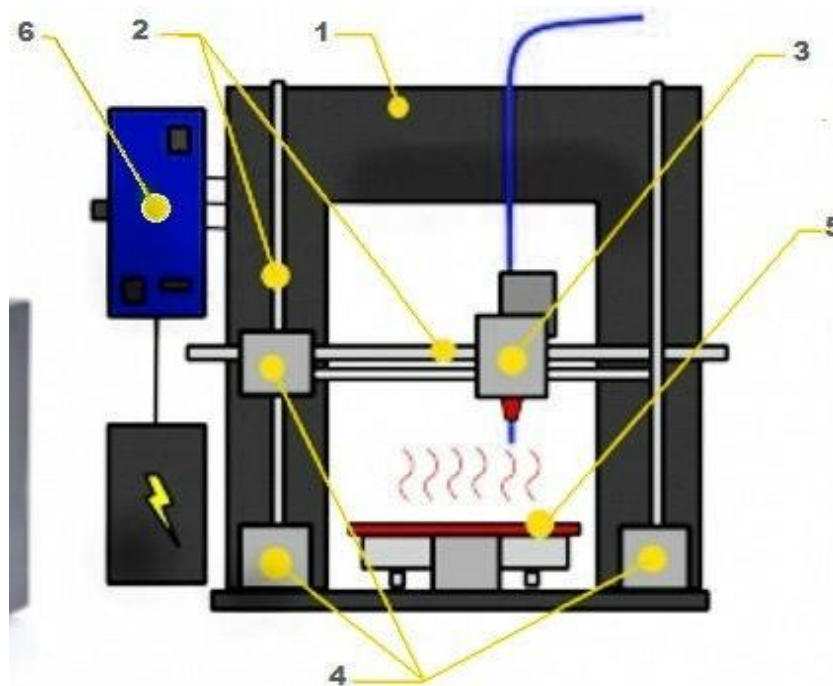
Типова конструкція 3D-принтера [18]
